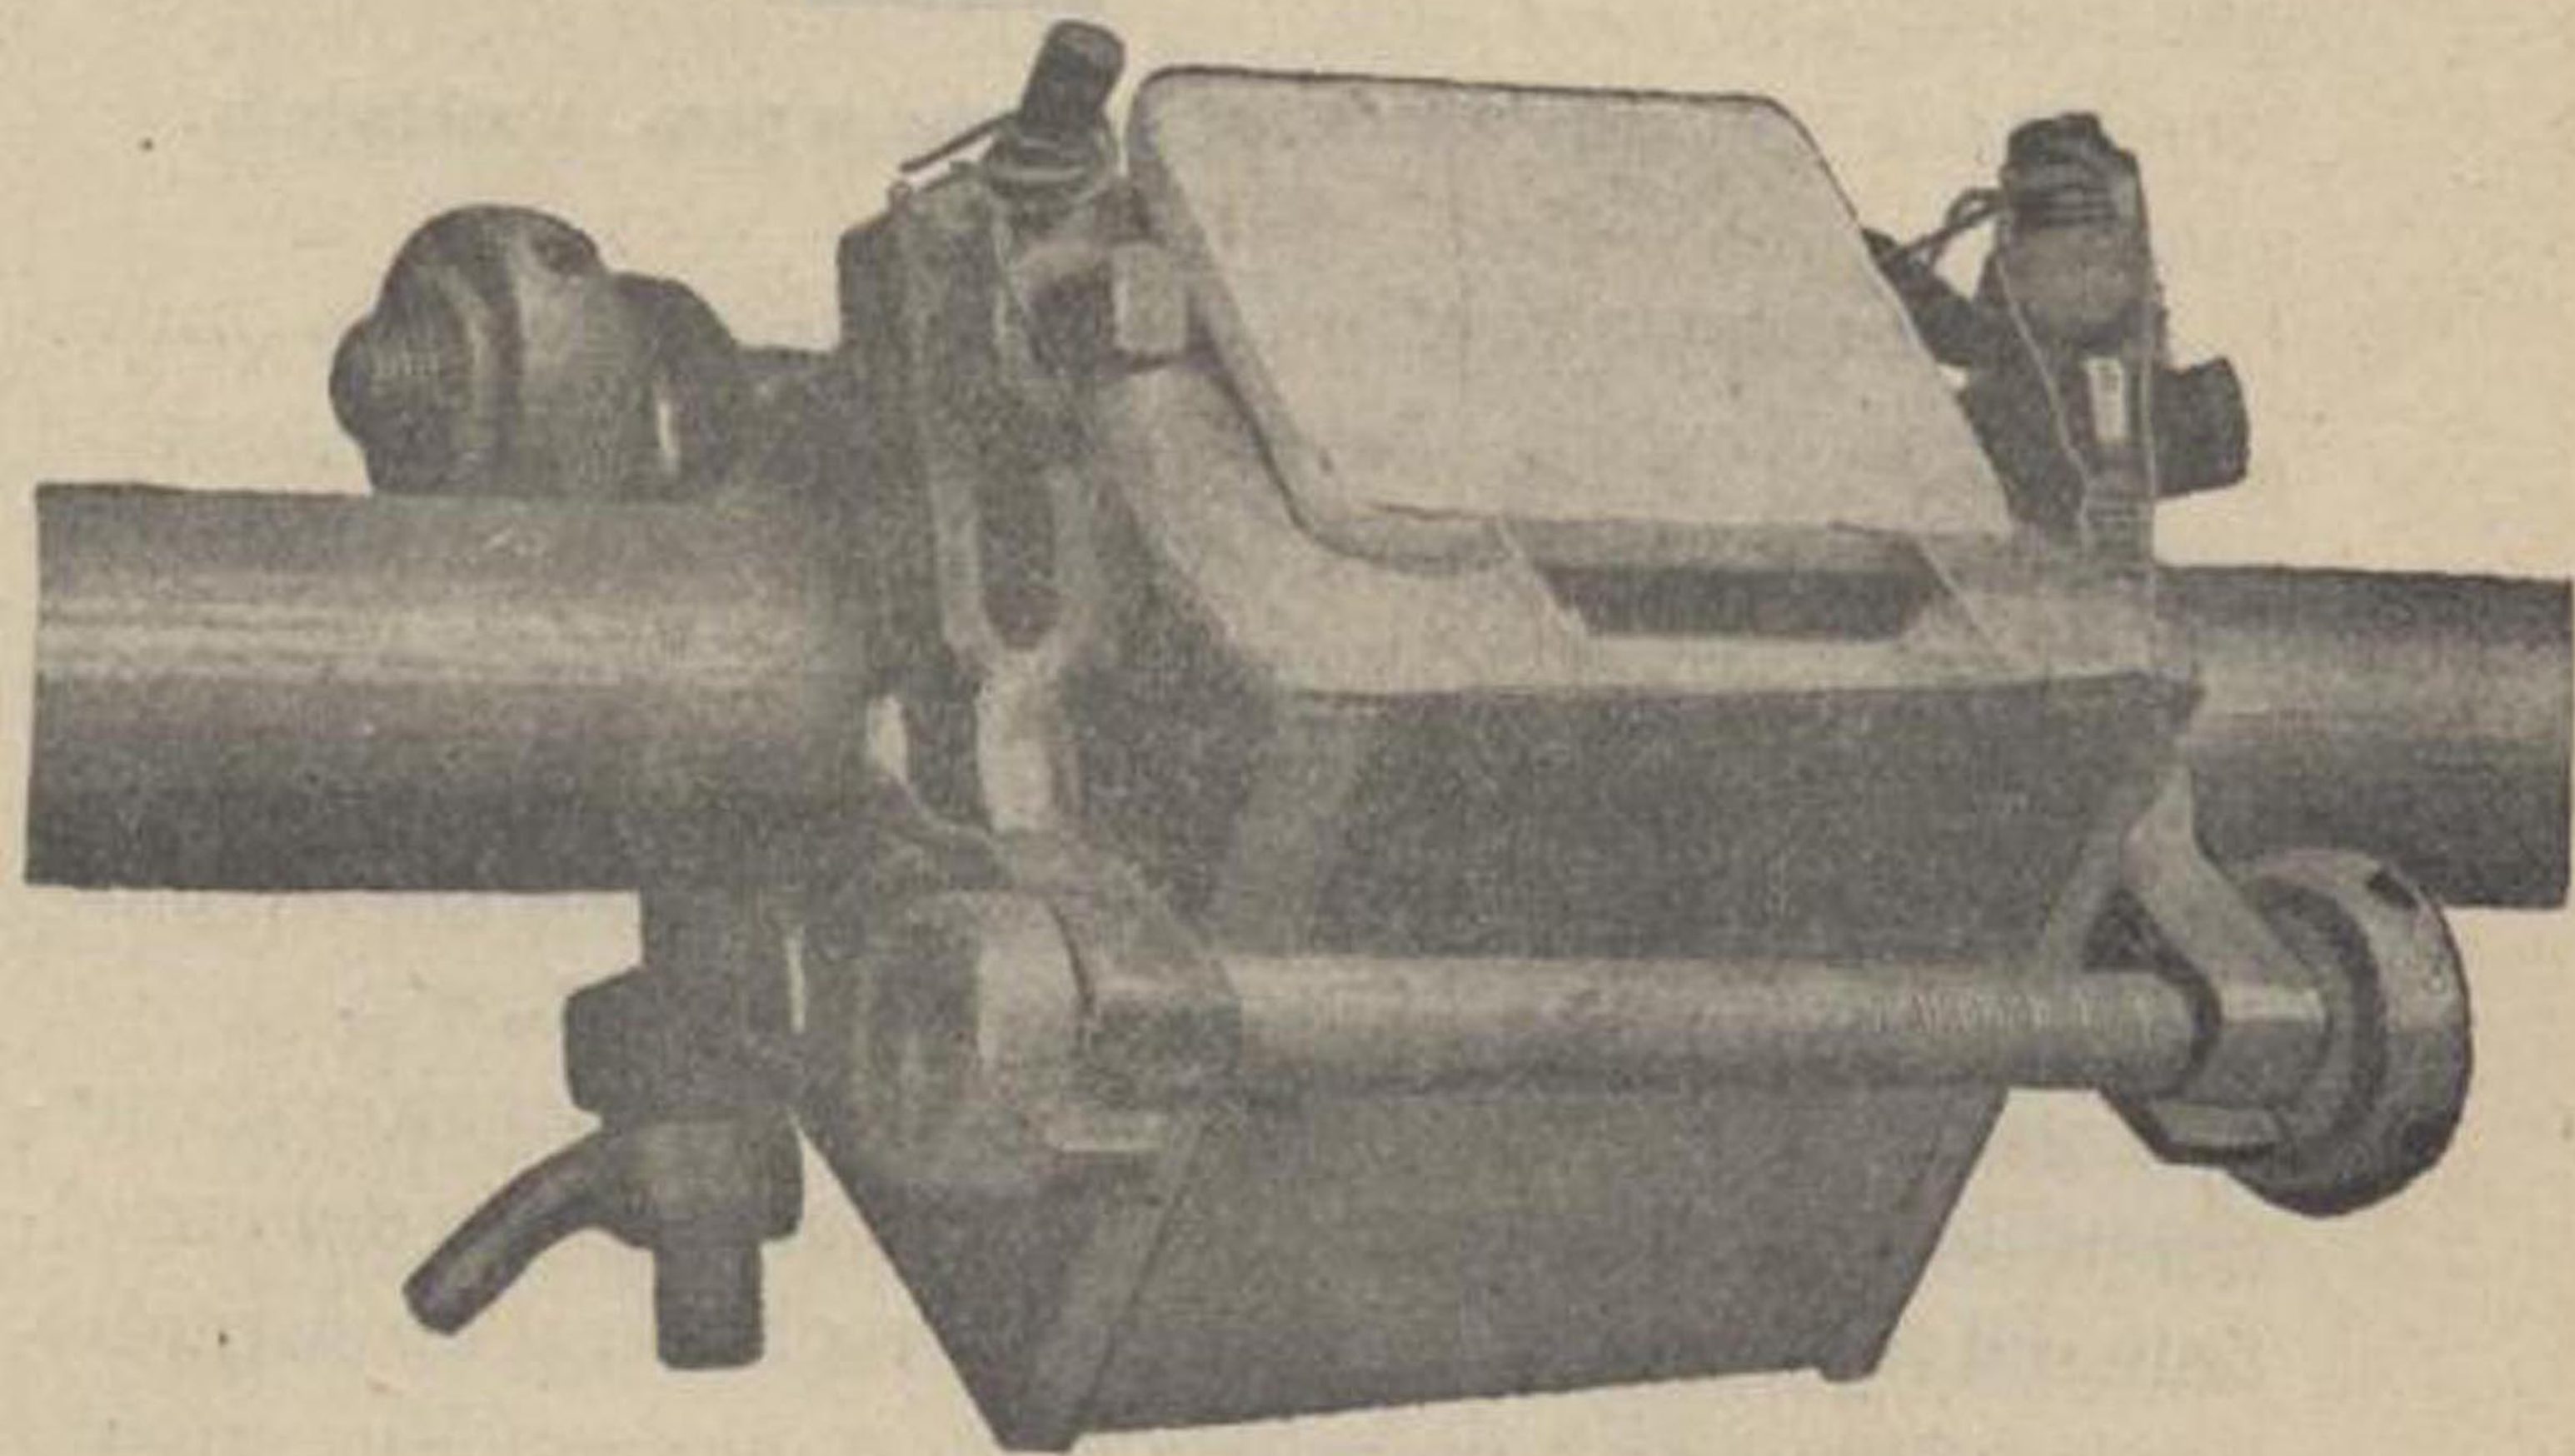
^a—Tubos horizontales preparados para la soldadura
